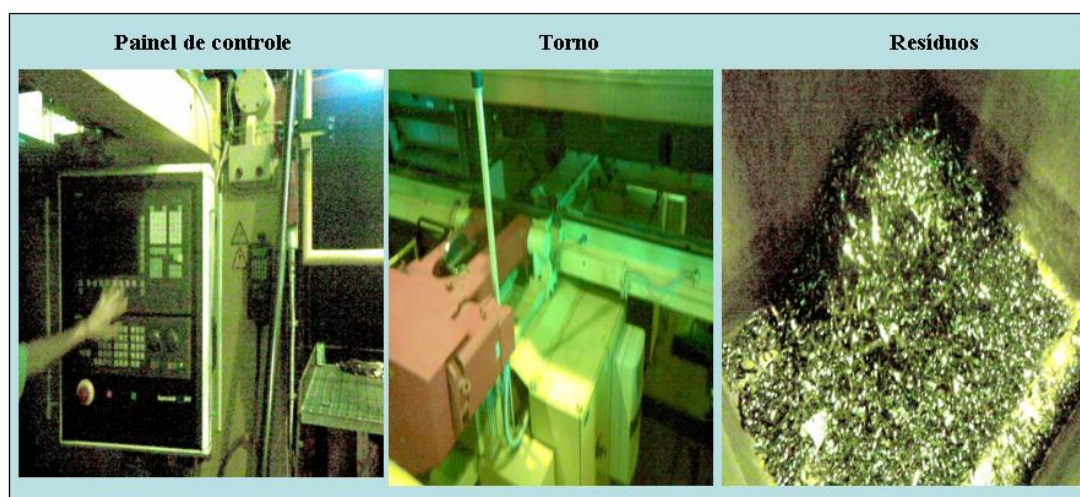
Usinagem de rodeiros com o torno CNC
